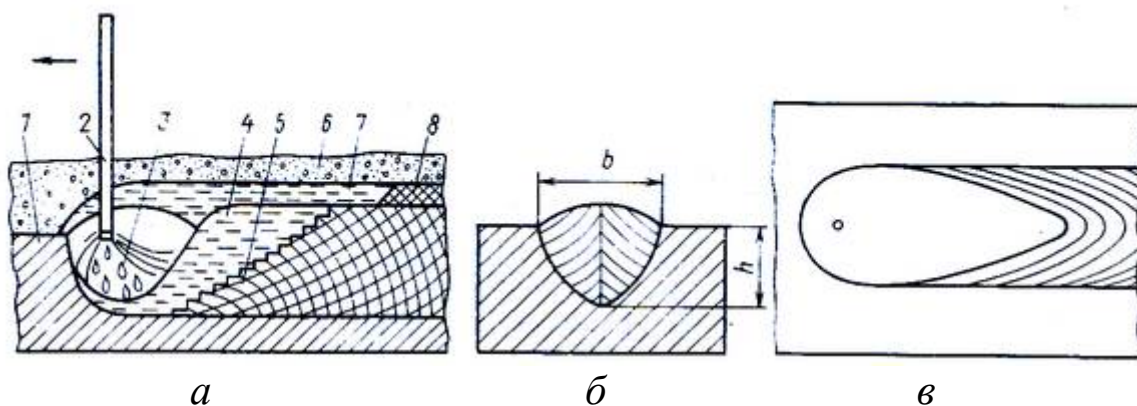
Схема зоны сварки под флюсом: *a* – разрез вдоль оси шва; *б* – поперек шва; *в* – сверху после удаления флюса и шлака; 1 – основной металл; 2 – электродная проволока; 3 – электродные капли; 4 – металл сварочной ванны; 5 – металл шва; 6 – флюс; 7 – жидкий флюс (шлак); 8 – твердый шлак; *b* – ширина шва; *h* – высота шва
